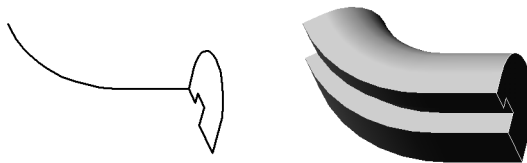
Эскизы и элемент, образованный кинематической операцией
